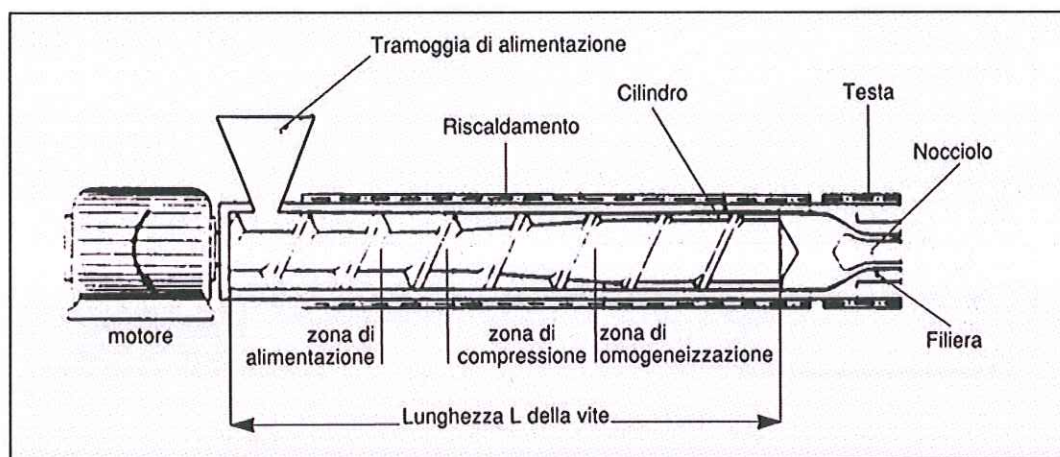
Sezione longitudinale di un estrusore per la fabbricazione di tubi profilati
